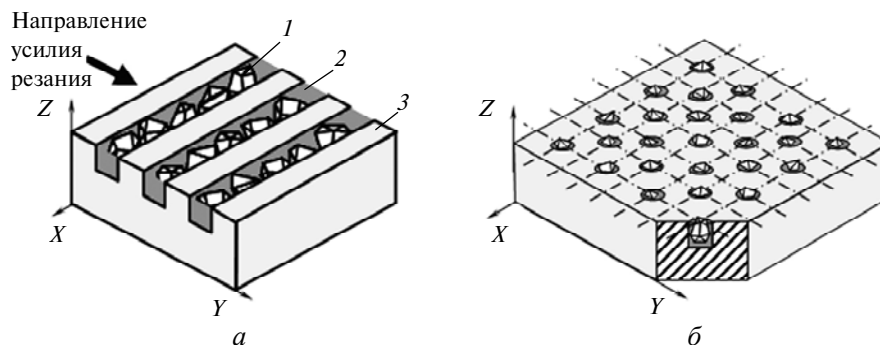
Алмазный твердосплавный высокомодульный композиционный материал АВКМ: 1 – алмазное зерно; 2 – припой; 3 – пластина твердого сплава марки ВК6; канавки (а) и отверстия (б) в материале.
